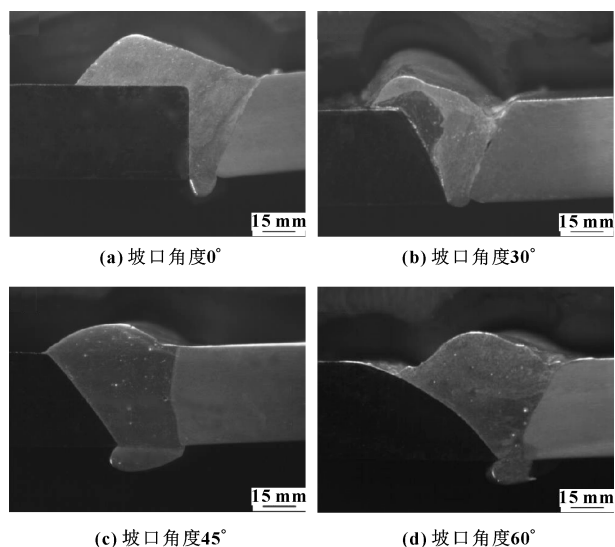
不同 Q890D 钢侧坡口角度的焊接接头横截面形貌
